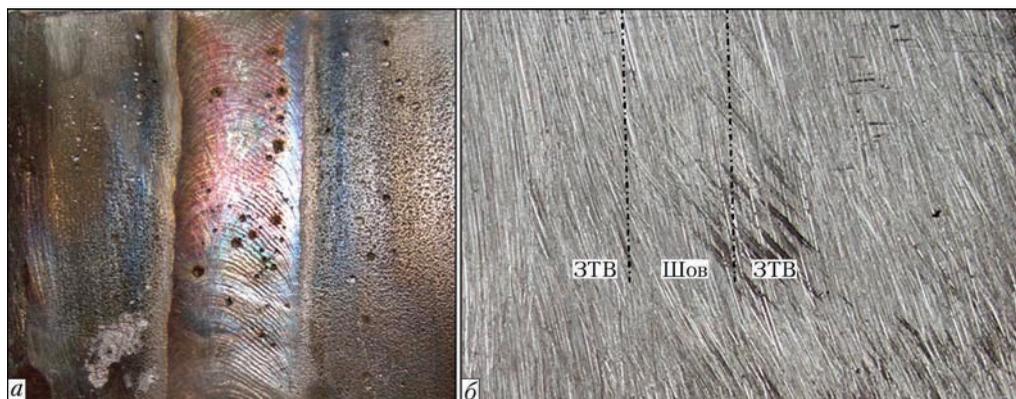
Поверхность сварного соединения листовой стали 12X18H10T, испытанного на питтинговую коррозию в течение 5 ч в состояниях после сварки (а) и абразивной обработки (б)
